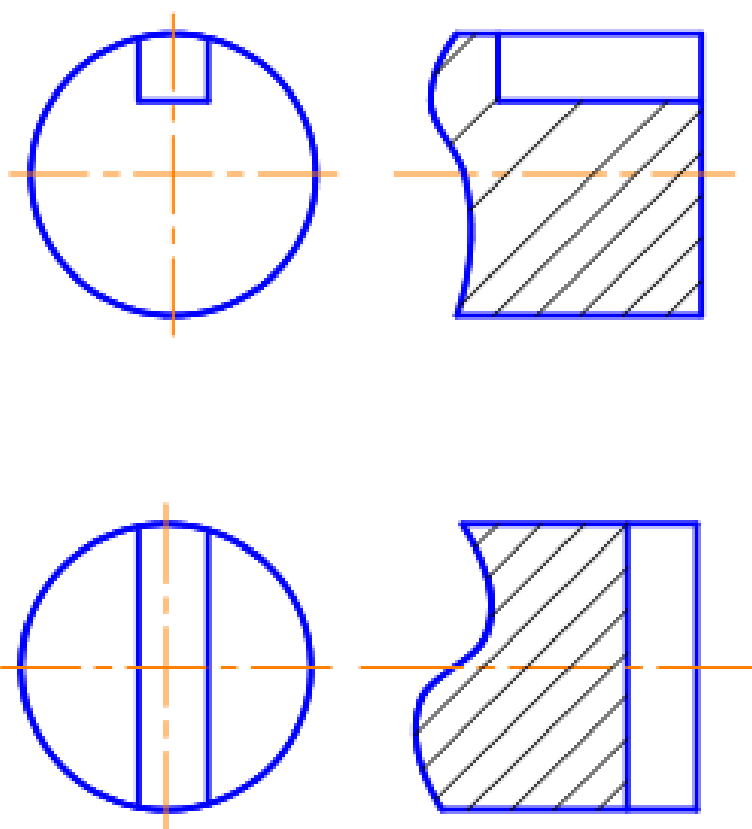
Два варианта шпоночных пазов на детали типа вал
